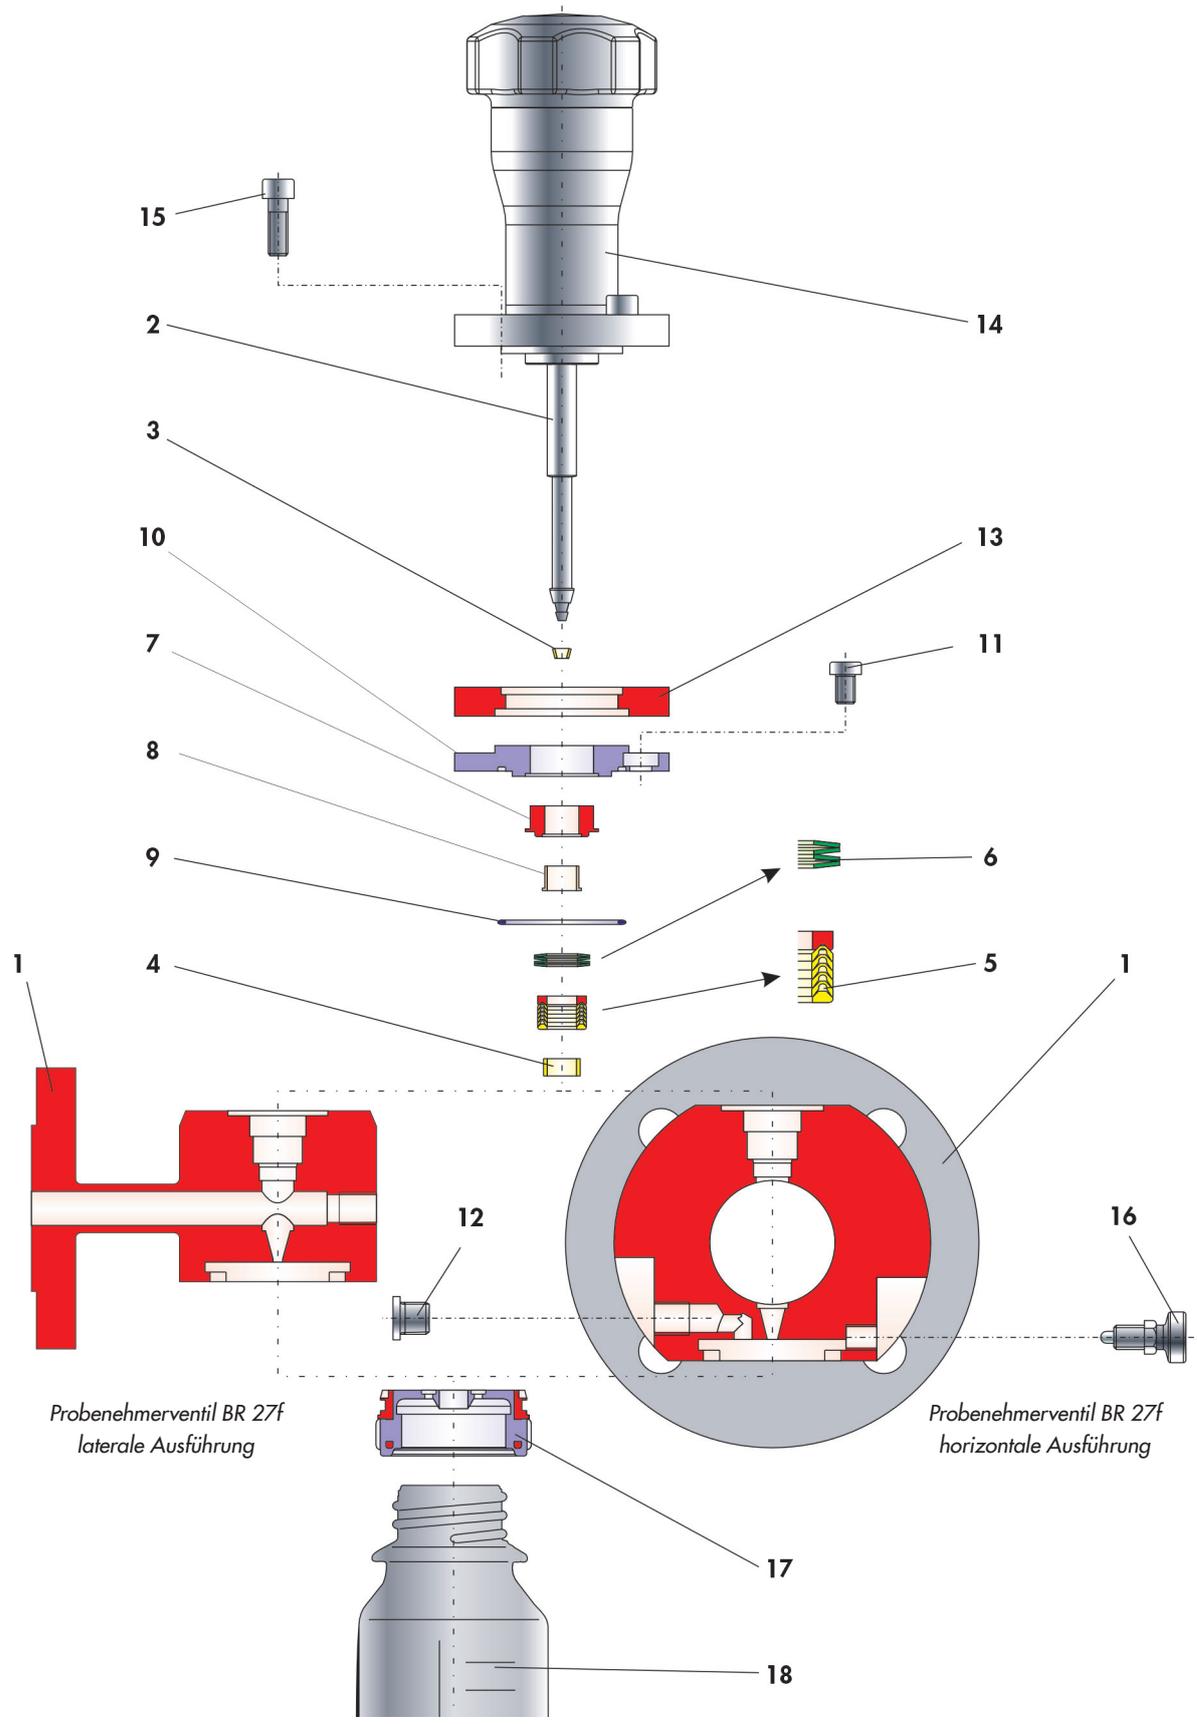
Explosionszeichnung des Probenehmerventils BR 27f
